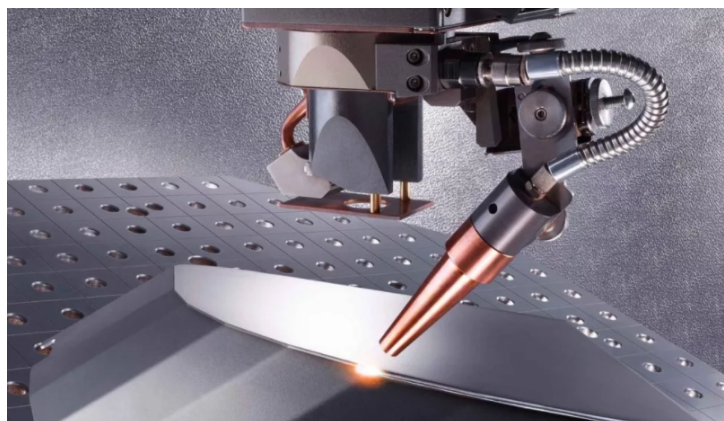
Soldagem a LASER de geometrias complexas (THE..., 2020).
